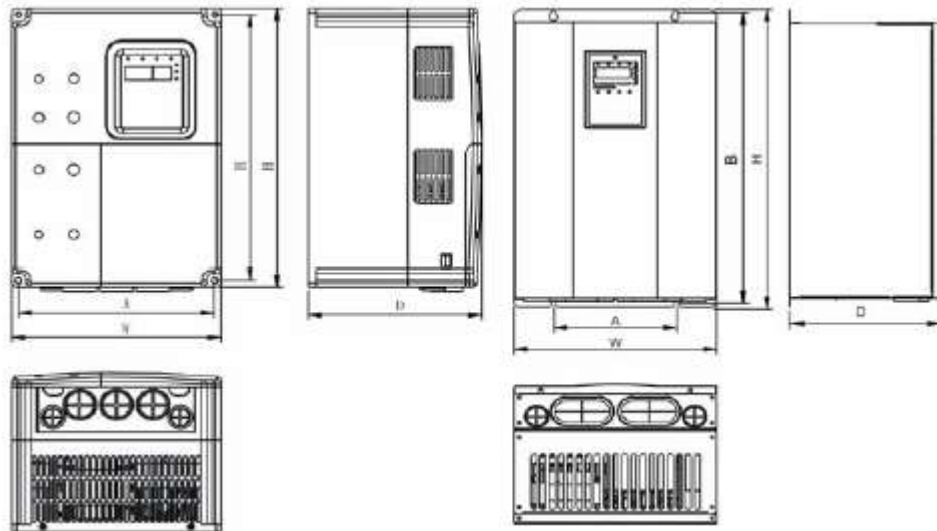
Габаритные размеры (0,75–15 кВт)
